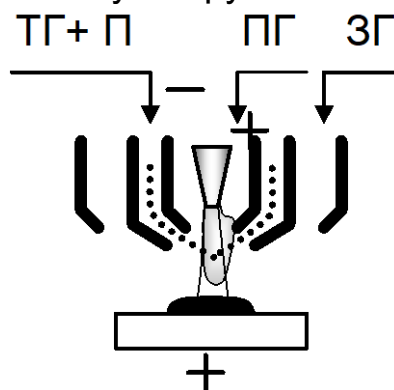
Схема двухдуговой плазменной наплавки (с постоянно включенной пилотной дугой); ПГ – плазмообразующий газ, ЗГ – защитный газ, ТГ – транспортирующий газ; П – порошок
